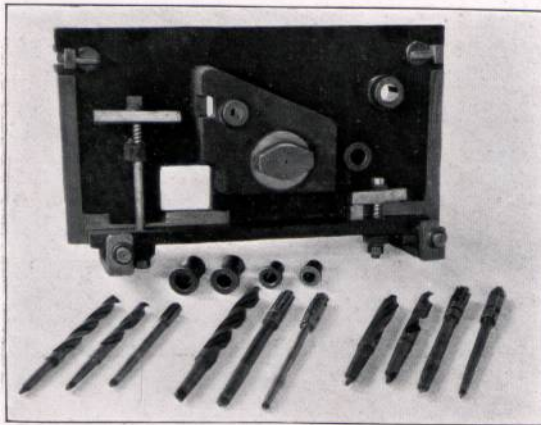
Einspannvorrichtung, Werkzeuge und Führungsbuchsen zu Abbildung 68.
